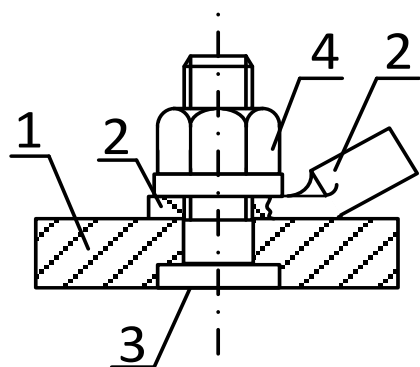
Контактное соединение шин ШЗУП-МУВ, ШЗУП-МВ и ШЗУП-МДВ через винт запрессовочный (1 - медная шина; 2 – кабельный наконечник; 3 – винт запрессовочный; 4 – гайка с зубчатым фланцем).
